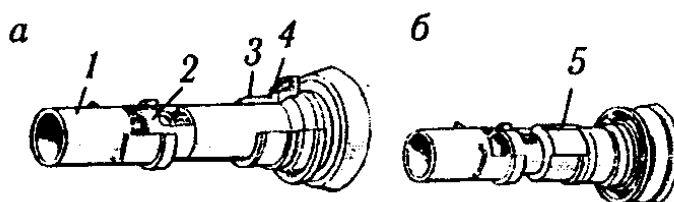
Расположение приспособлений при установке внутренних колец: а – заднего подшипника; б – переднего подшипника;
